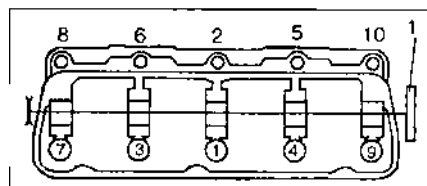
Схема затяжки болтов крепления головки цилиндров:
